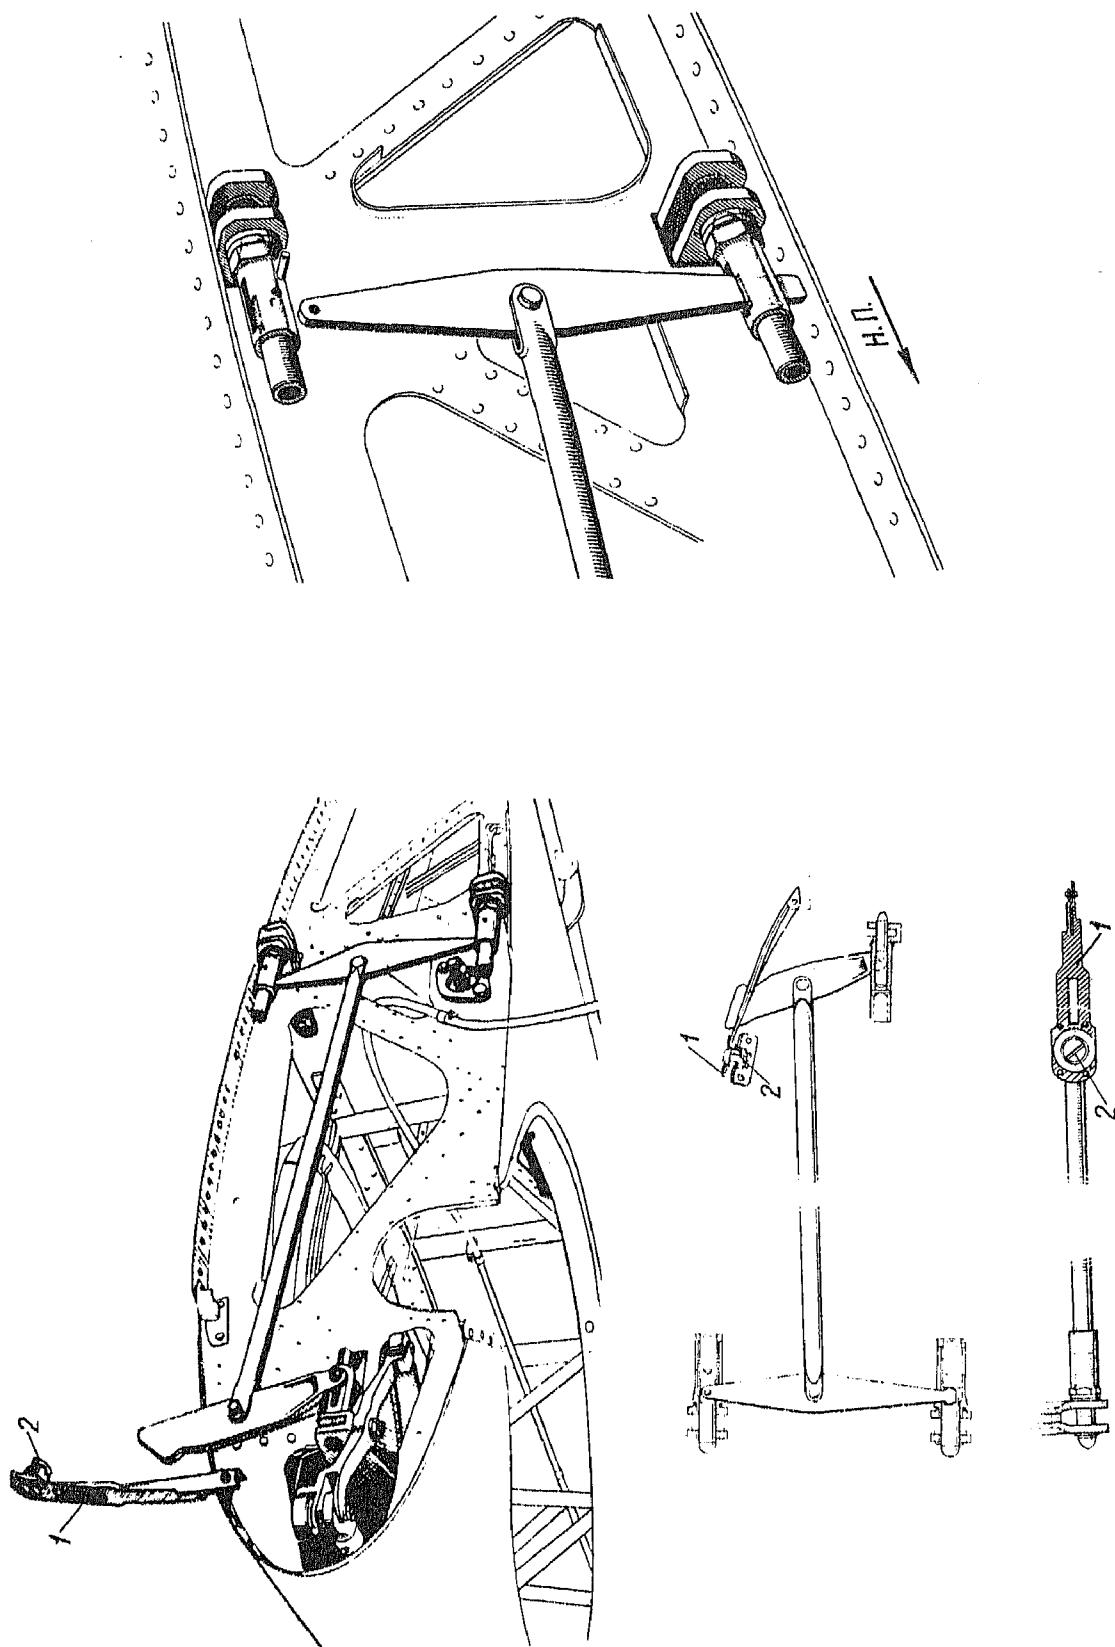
Общий вид кабины и механизм аварийного сбрасывания фонаря:
